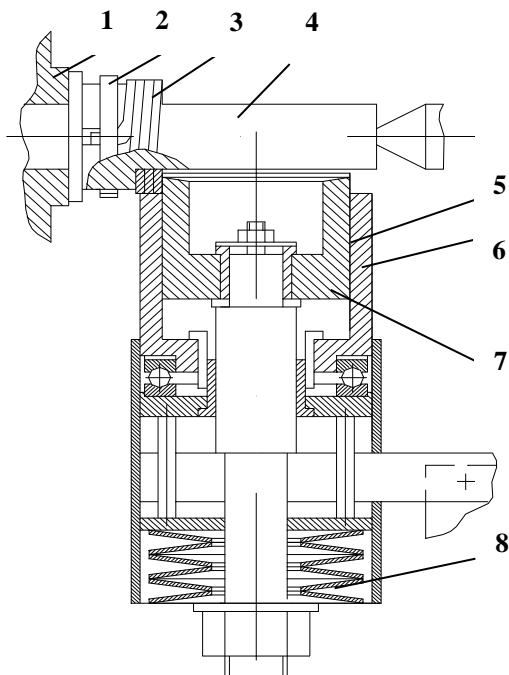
Пристрій для утворення заготовок циліндричних зубчастих коліс.
